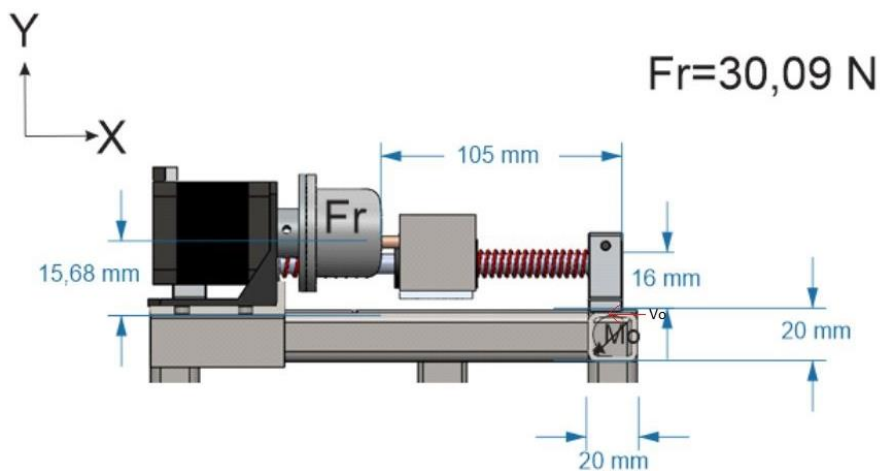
Esquema de dimensiones y fuerzas leva cilíndrica.
